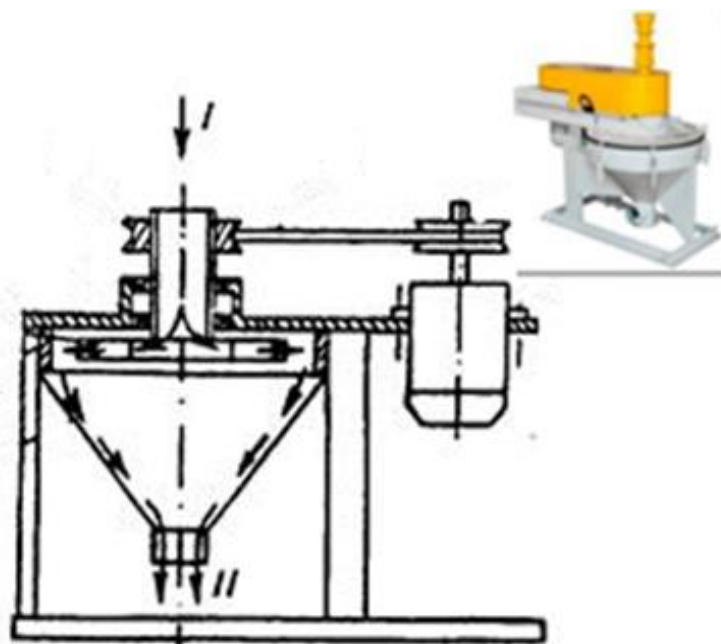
Схема и общий вид центробежного шелушителя [2]
